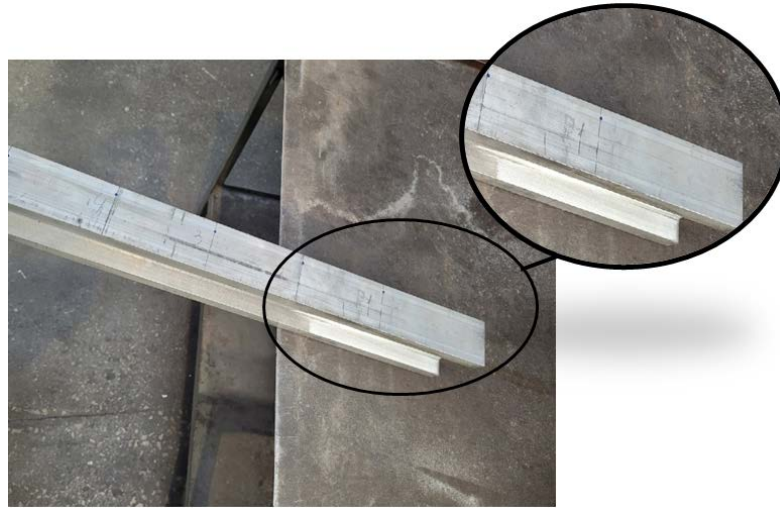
Разметка профиля для измерения деформаций для выполнения адаптивной калибровки
